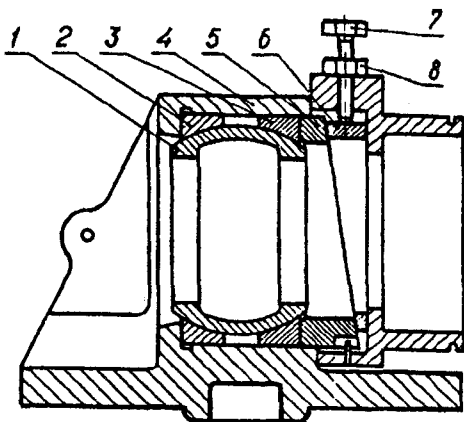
Устройство для регулировки зазора в подшипнике скольжения (патент № 4225198, США)
